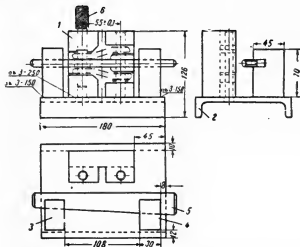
Кондуктор для рассверловки отверстий в звеньях теребилной цепи.
